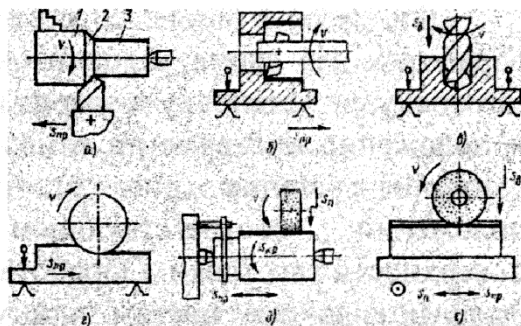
Схемы обработки заготовок: а — точением) б — растачиванием; в — сверлением; г — фрезерованием; д — шлифованием на круглошлифовальном станке; е — шлифованием на плоскошлифовальном станке
